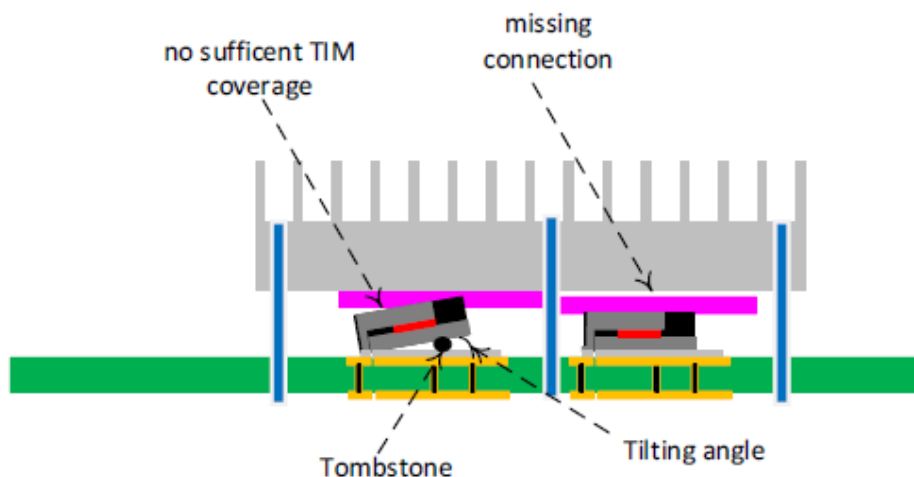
MOSFETs soldats a la PCB amb mal contacte amb el dissipador de calor. Font [10].
